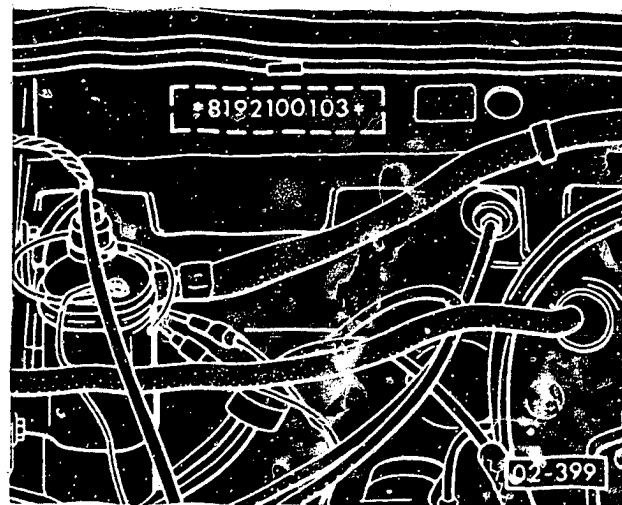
Die Karosserienummer ist am Blech der Querwand des Motorraums eingeschlagen.
